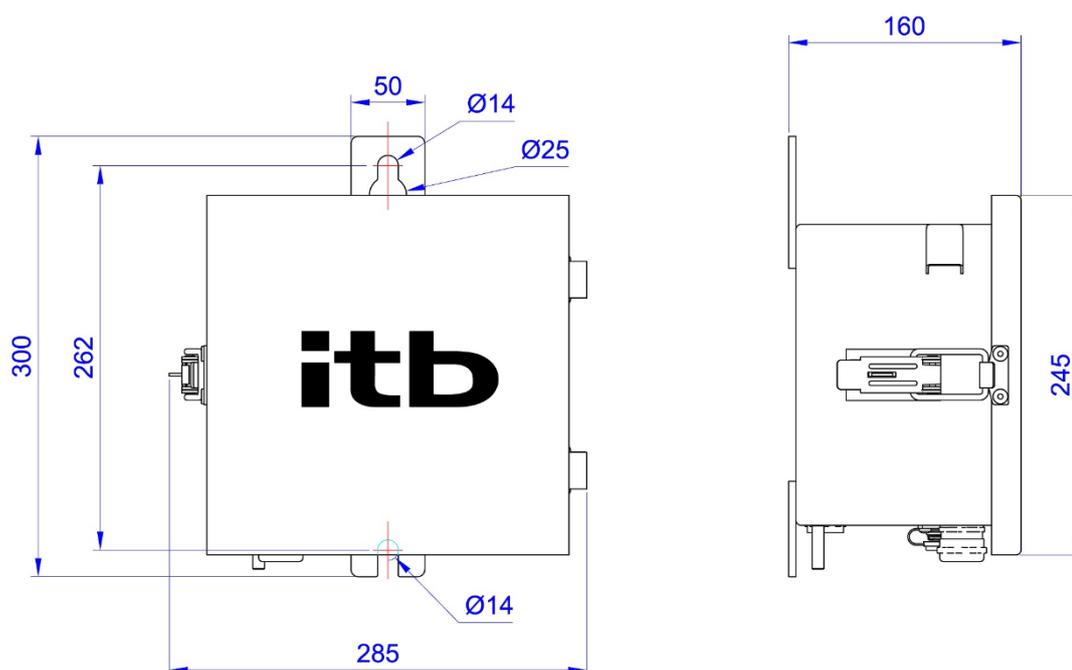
Dimensional externo da caixa auxiliar de passagem.
